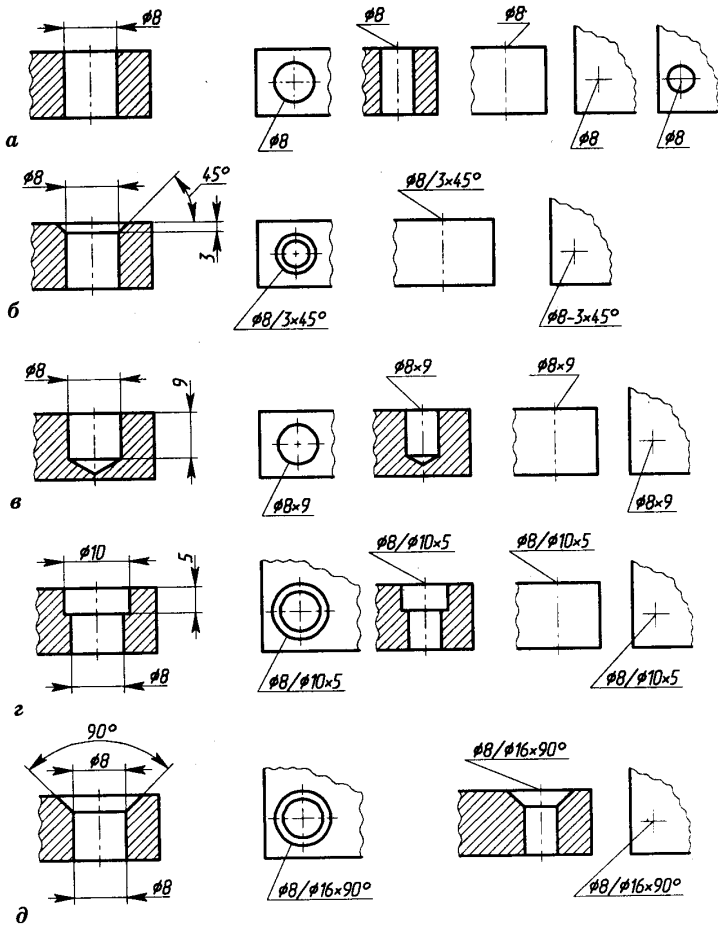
Варианты простановки размеров диаметра и глубины отверстий:
